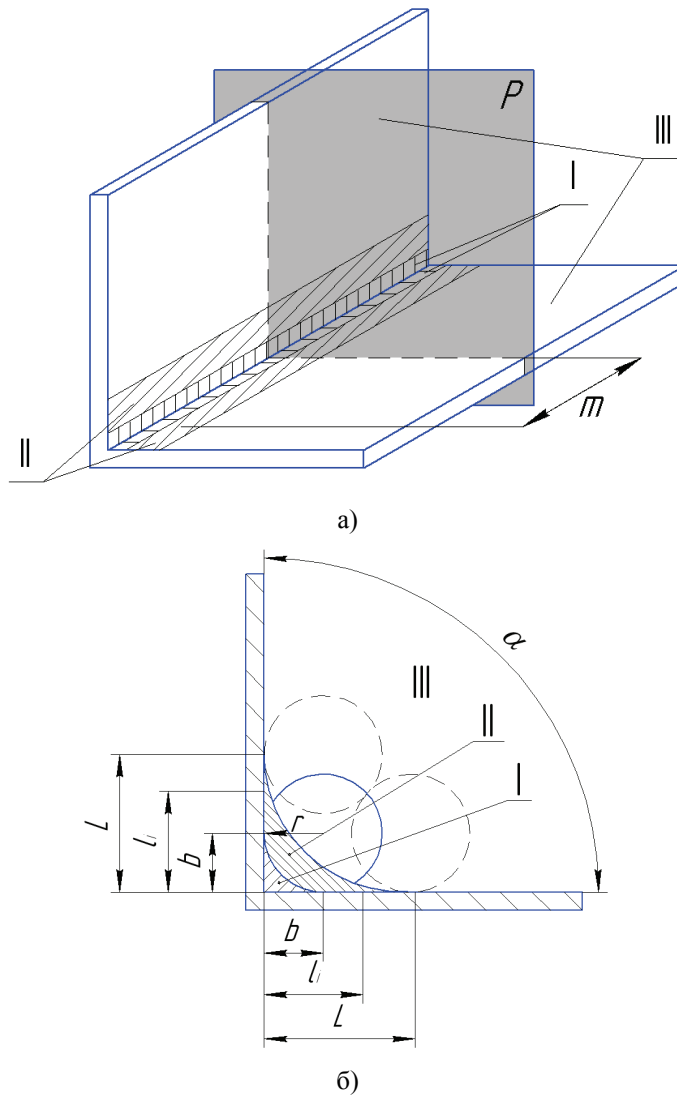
Схема контакта обрабатывающих тел с деталью «уголок» в зоне сопряжения обрабатываемых поверхностей: а – общий вид детали; б – поперечное сечение детали
